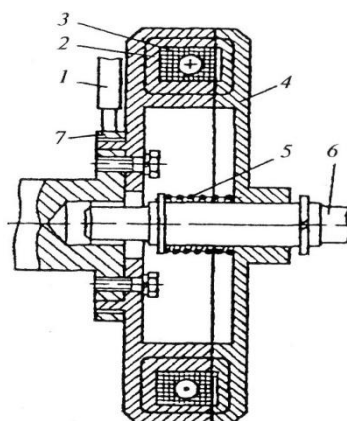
Схема электромагнитного сцепления: 1 – щетка; 2 – сердечник; 3 – обмотка; 4 – якорь; 5 – пружина; 6 – первичный вал; 7 – коллекторные кольца
